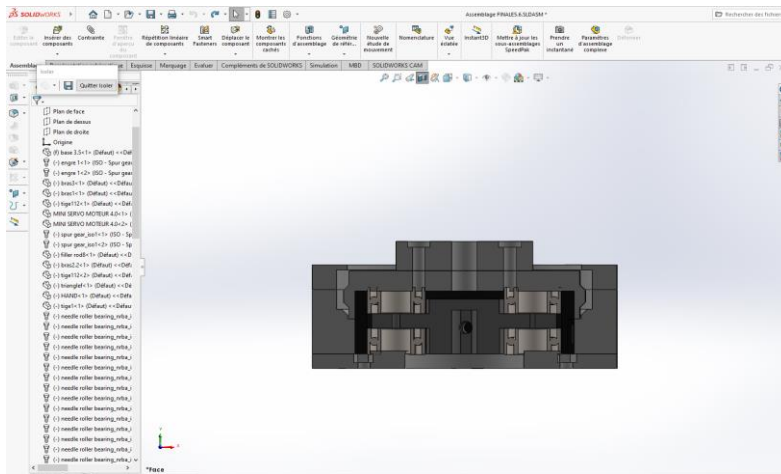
Vue en coupe de l'ensemble du réducteur Harmonic Drive Gearbox
